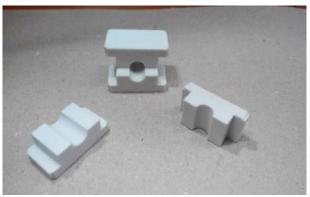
Керамические изоляторы для автоматической сварки биметаллических трубчатых элементов
